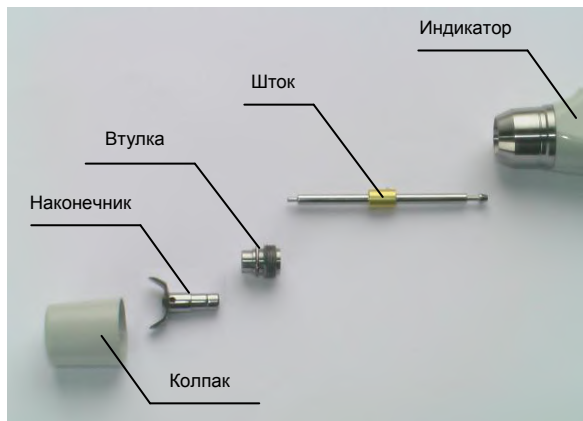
Подготовка индикатора к очистке штокового механизма
